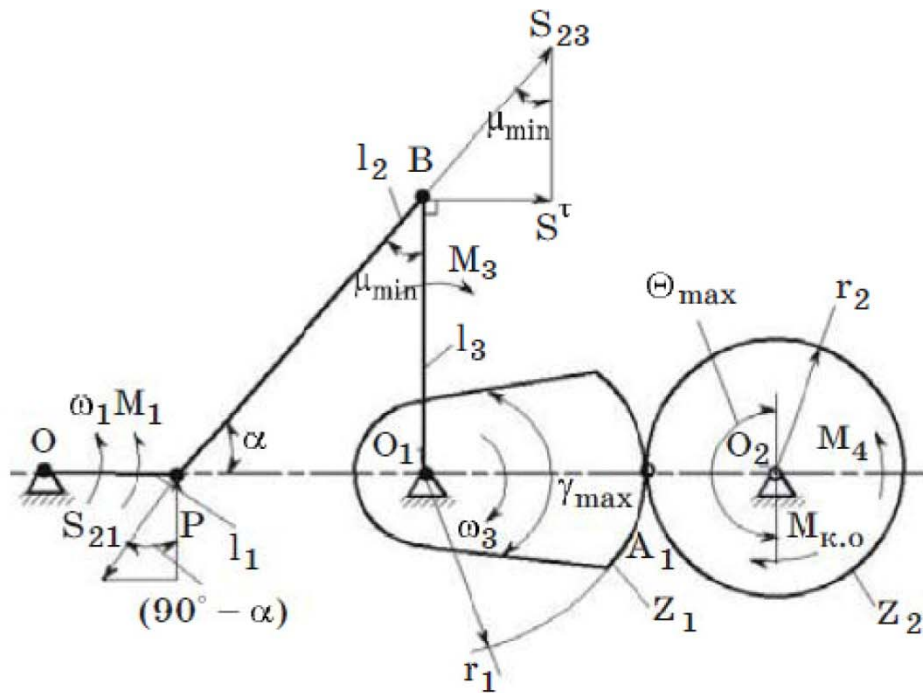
Розрахункова схема зубчато-важильного механізму
